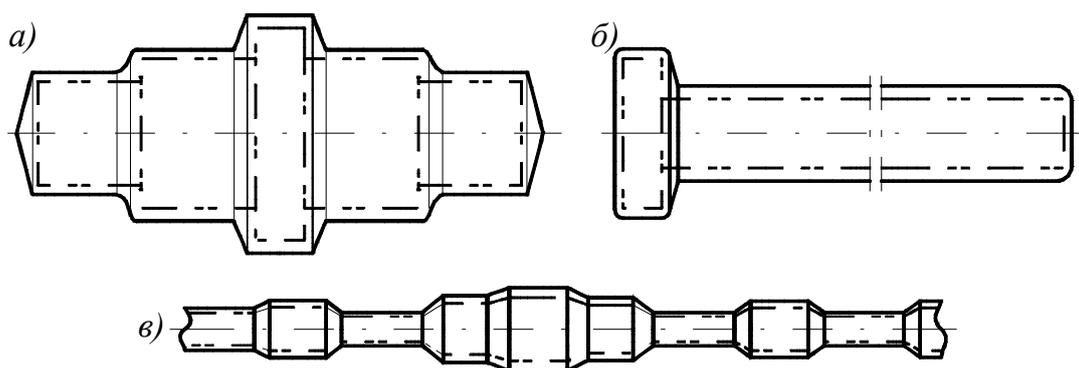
Заготовки, полученные методами: *a* – штамповкой в штампах; *б* – штамповкой на горизонтально-ковочной машине; *в* – поперечно-винтовой прокаткой
